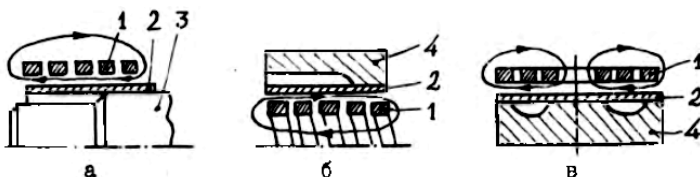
Технологические схемы МИОМ: а – обжим, б – раздача, в – листовая штамповка: 1 – индуктор; 2 – заготовка; 3 – оправка; 4 – матрица
